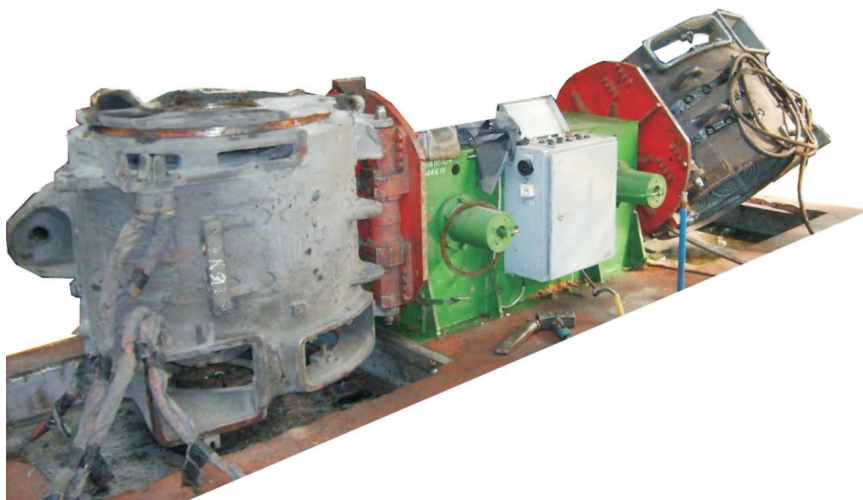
Кантователь для разборки, ремонта и сборки тягового электродвигателя ТЛ-2К1
